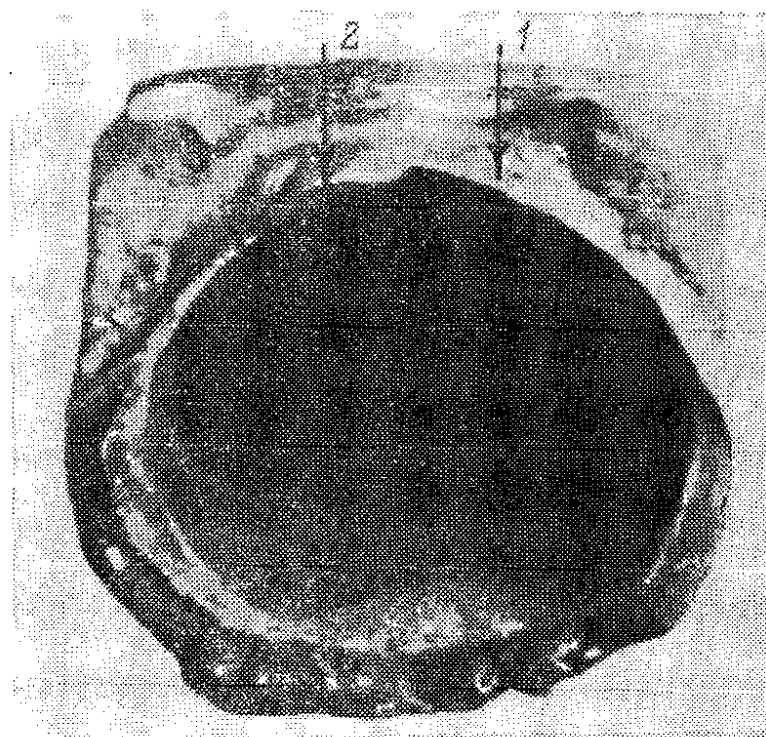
Поверхность разрушения правой отливки (см. рис. 131). Сварной шов сверху, интенсивное порообразование снизу (примерно в 1/2 величины)
